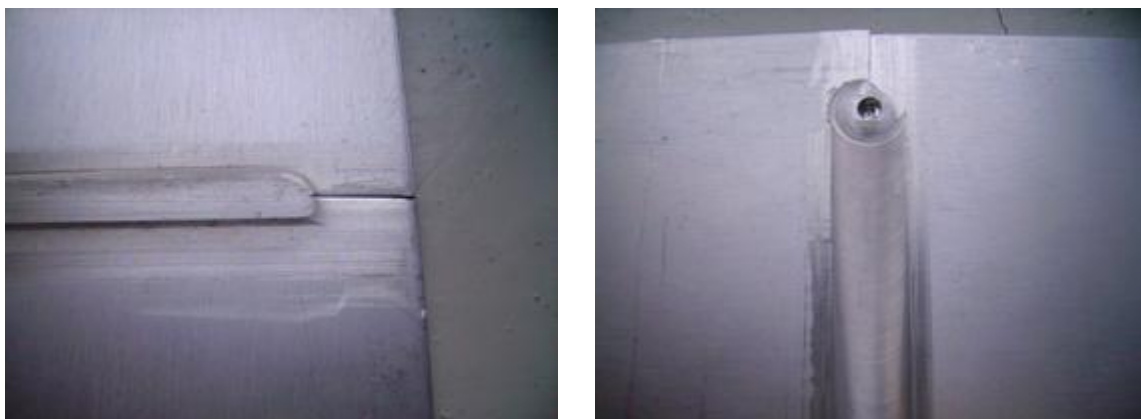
Образцы сплава АМГ6 толщиной 4 мм сваренные перемешивающей сваркой трением. Слева с лицевой стороны, справа с изнаночной.
